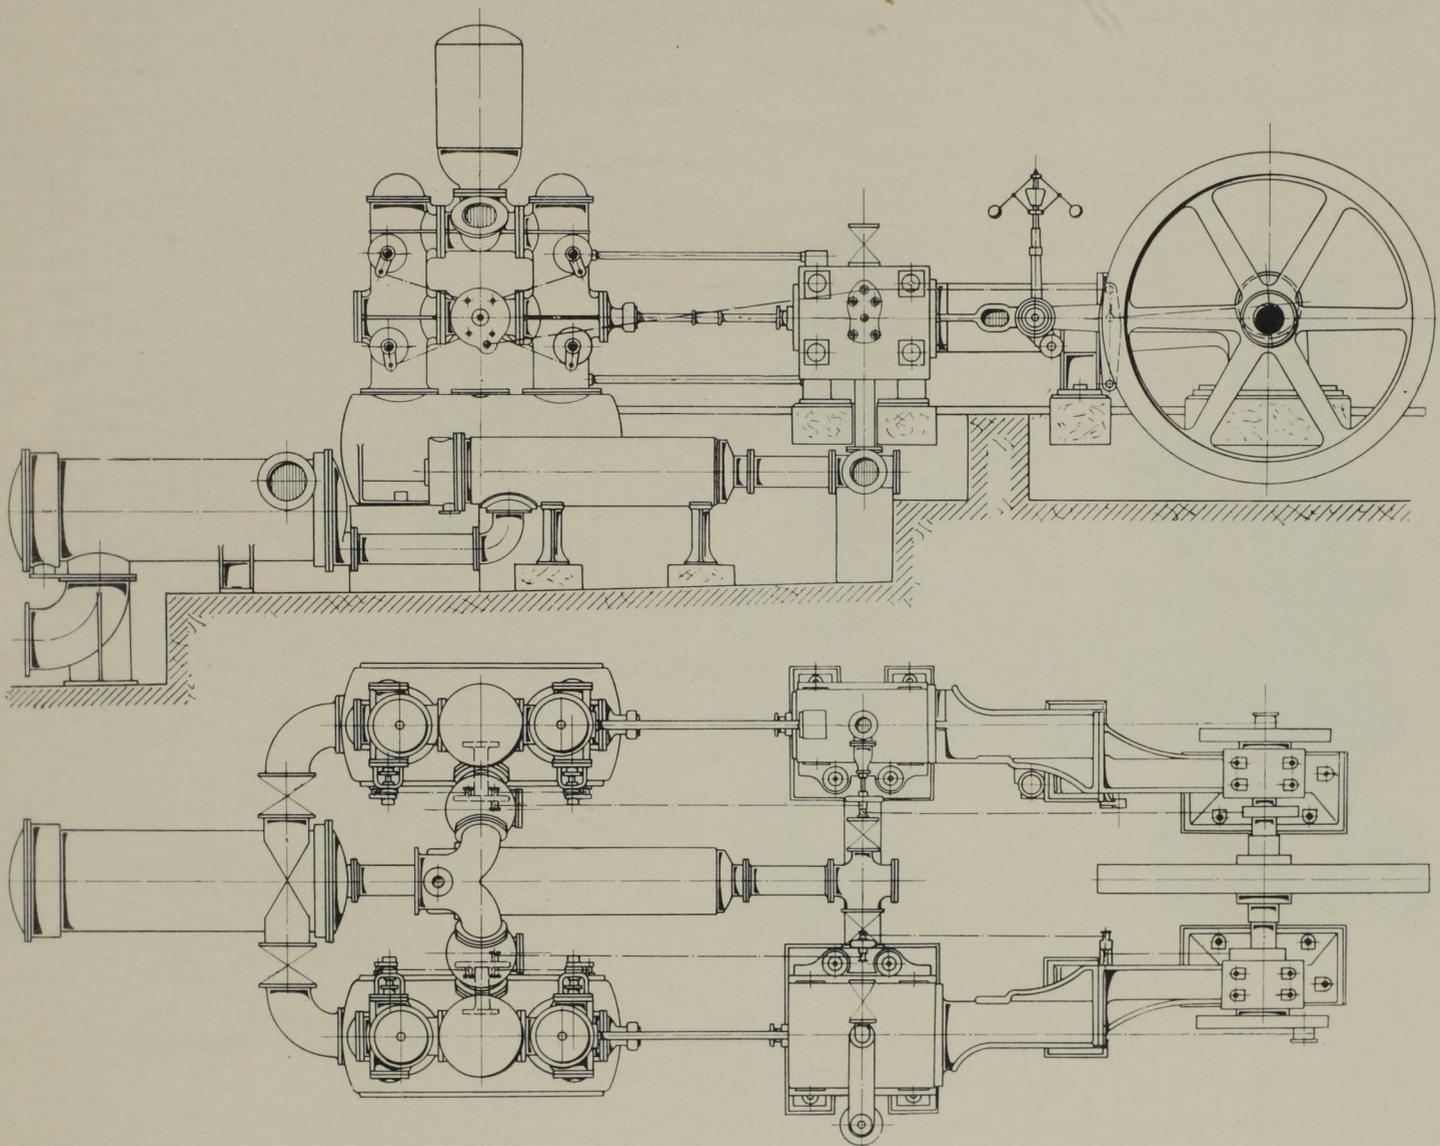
Seitenansicht und Grundriss der Pumpmaschine. Massst. 1:64.
